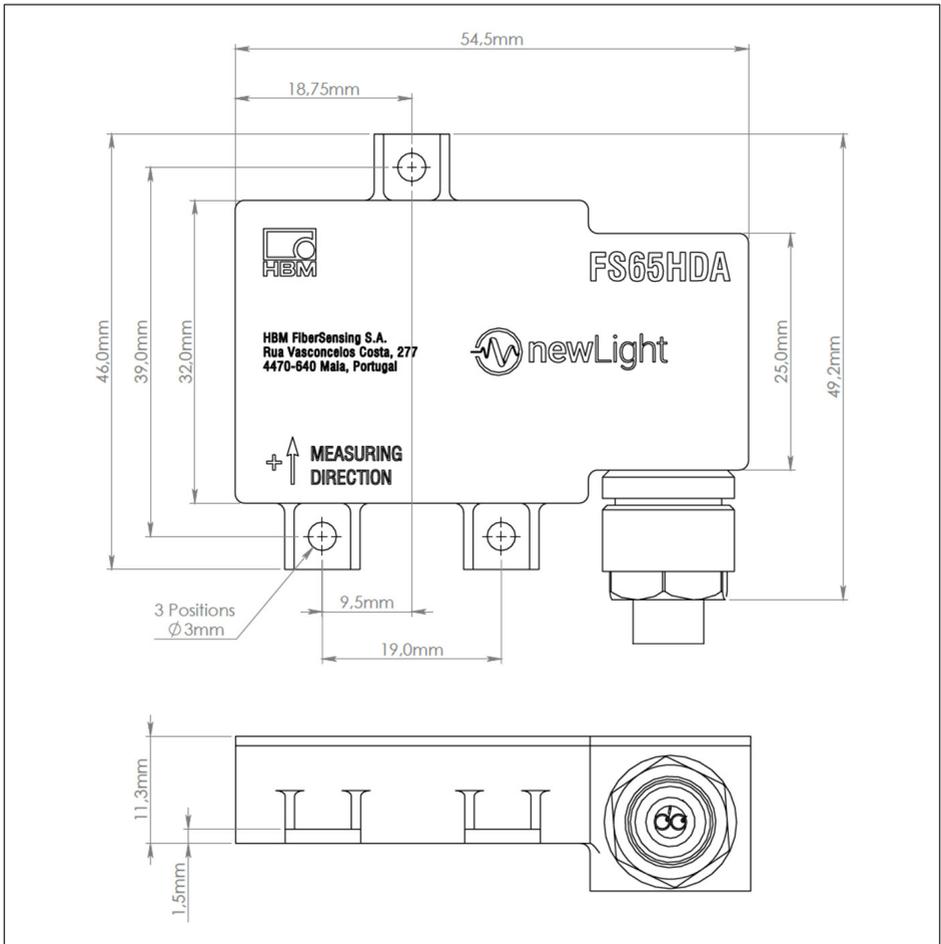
Dessin technique du capteur d'accélération Heavy Duty FS65HDA (dimensions en mm)
